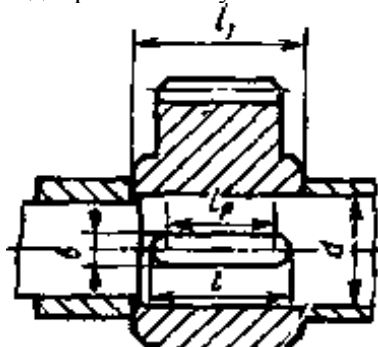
Зубчатое колесо, установленное на валу на призматической шпонке
